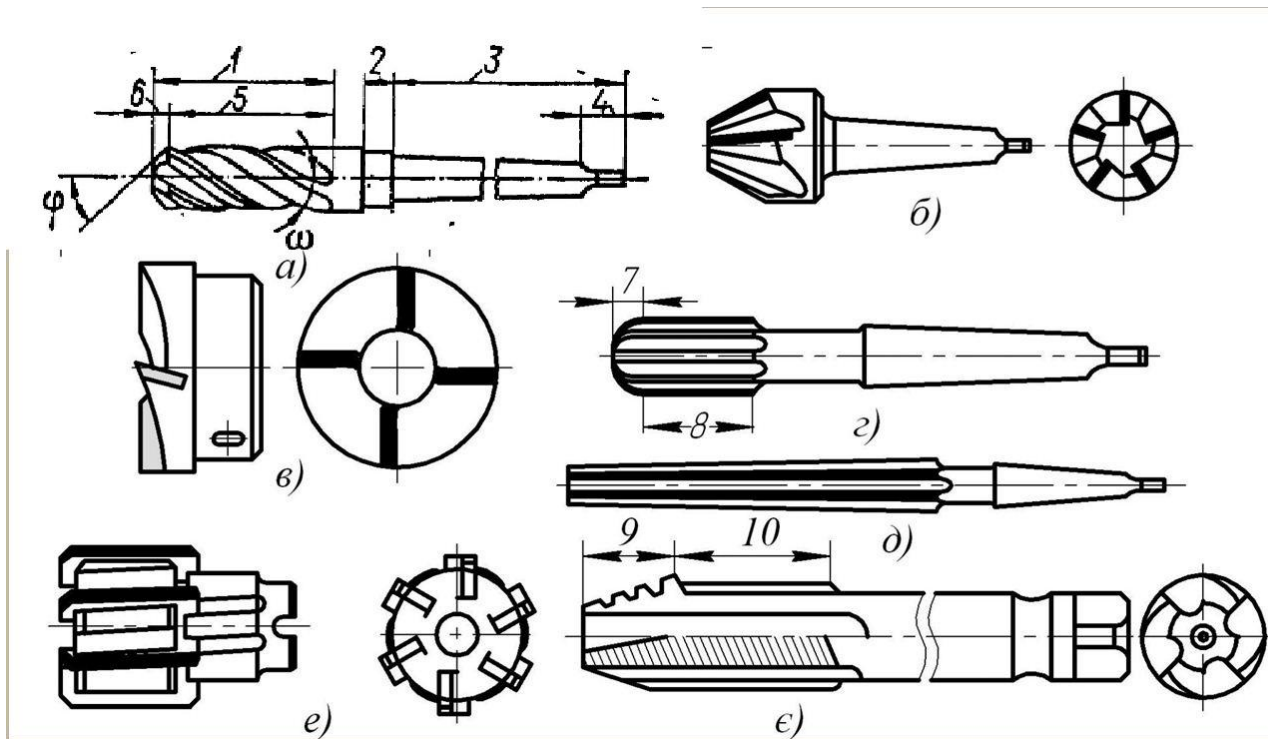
Інструменти для обробки отворів на свердлильних верстах: *а* - *в* - зенкери; *г* - *е* - розвертки; *є* - мітчик
